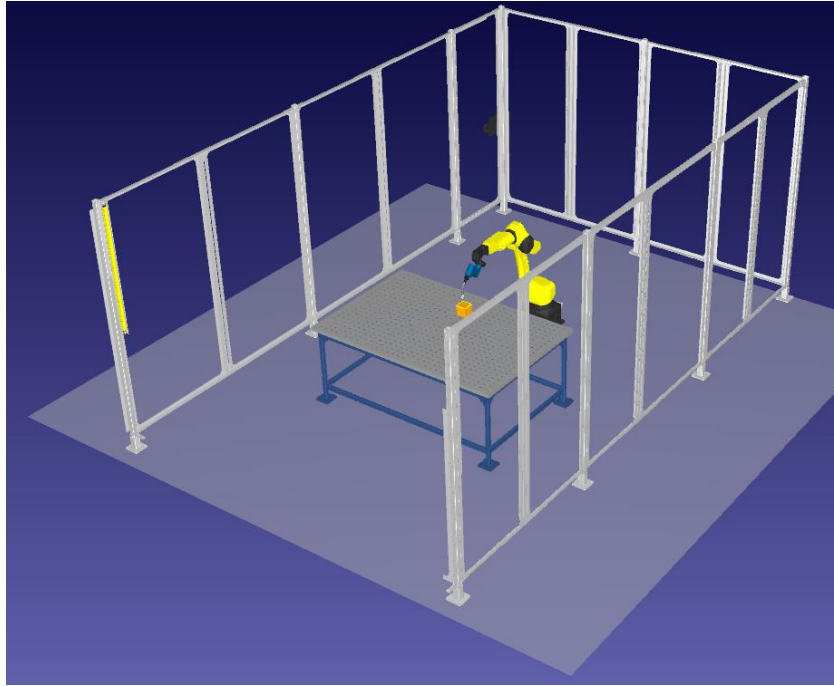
Célula de soldadura inicialmente idealizada
